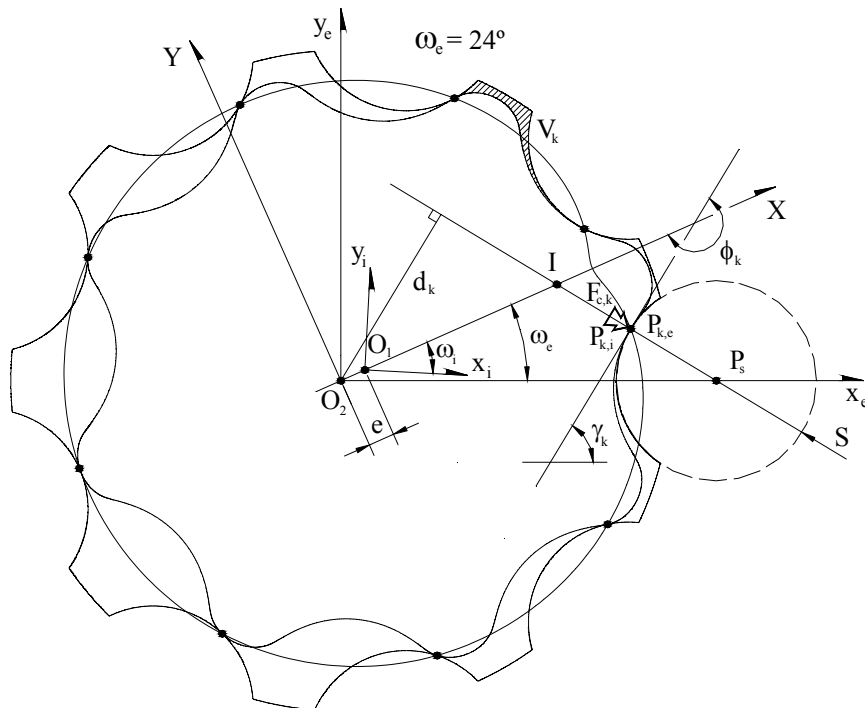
Geometría del engranaje mediante inversión cinemática
